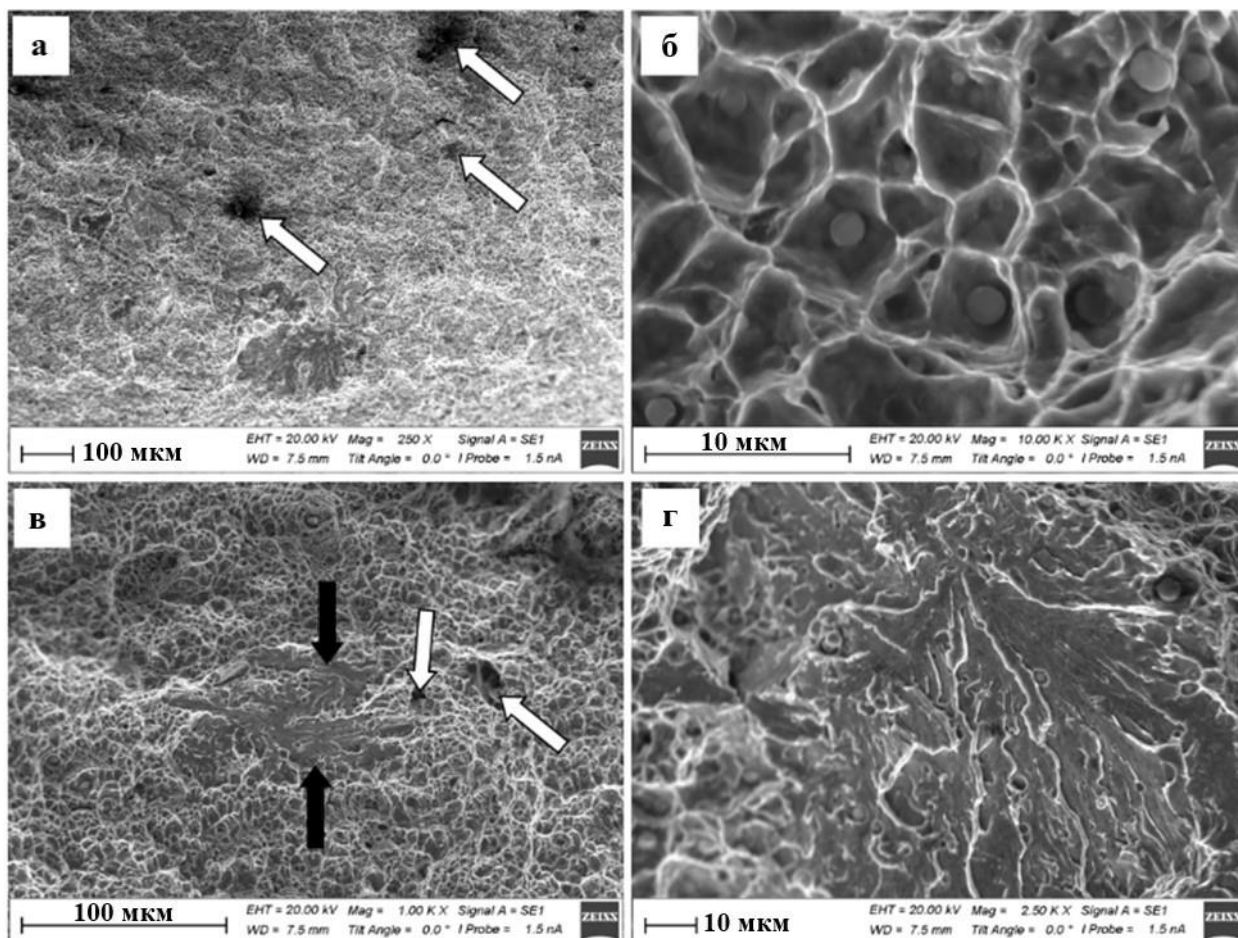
Электронно-микроскопическое изображение поверхности излома металла наплавки (светлыми стрелками указаны микро- и макропоры, несплошности металла, стрелками черного цвета – участки квазихрупкого излома)
